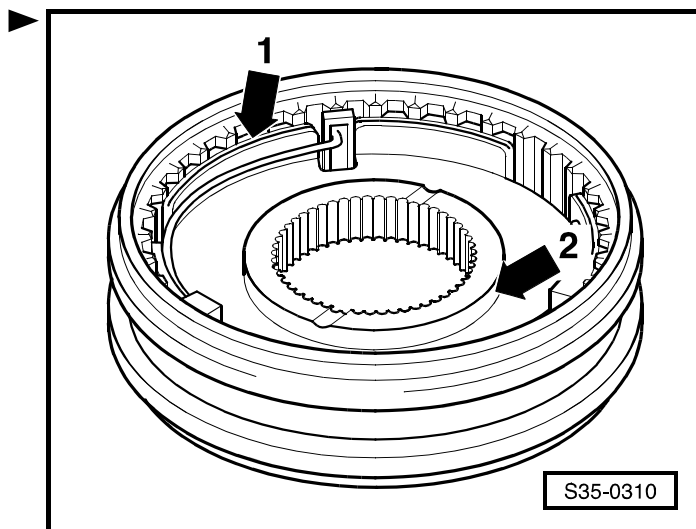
Запрессовывание скользящей муфты и каретки синхронизатора 1-ой и 2-ой передач
